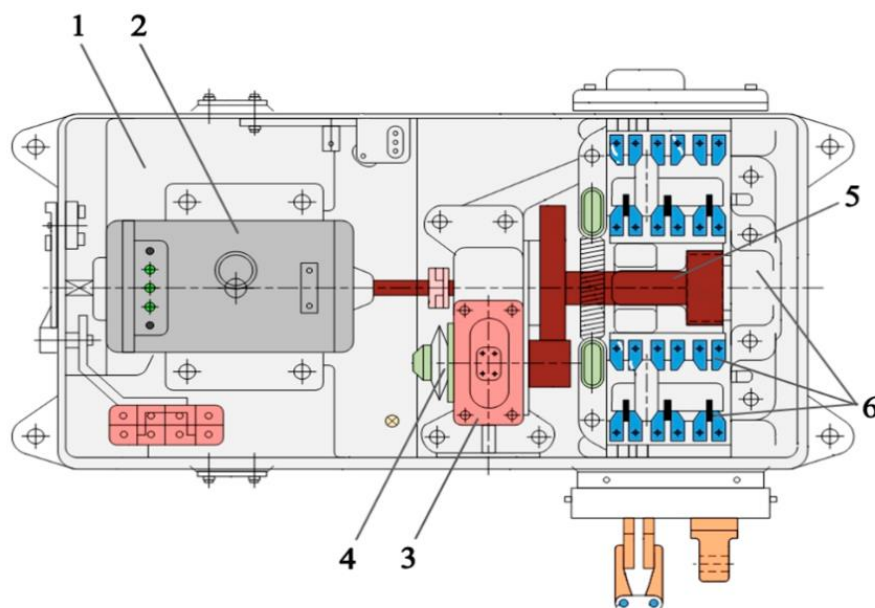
Основные части стрелочного электропривода: 1 – корпус;
